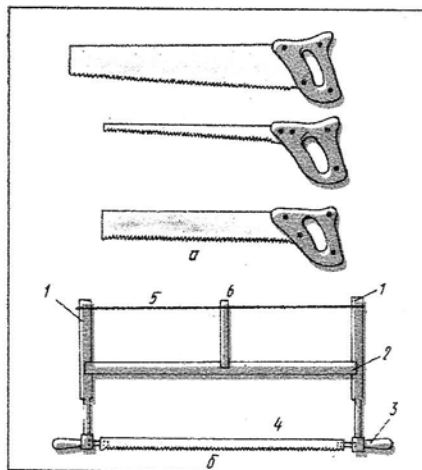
Ручные пилы: а — ножовки; б — лучковая; 1 — стойка; 2 — середник; 3 — ручка; 4 — полотно пилы; 5 — тетива; 6 — закрутка
